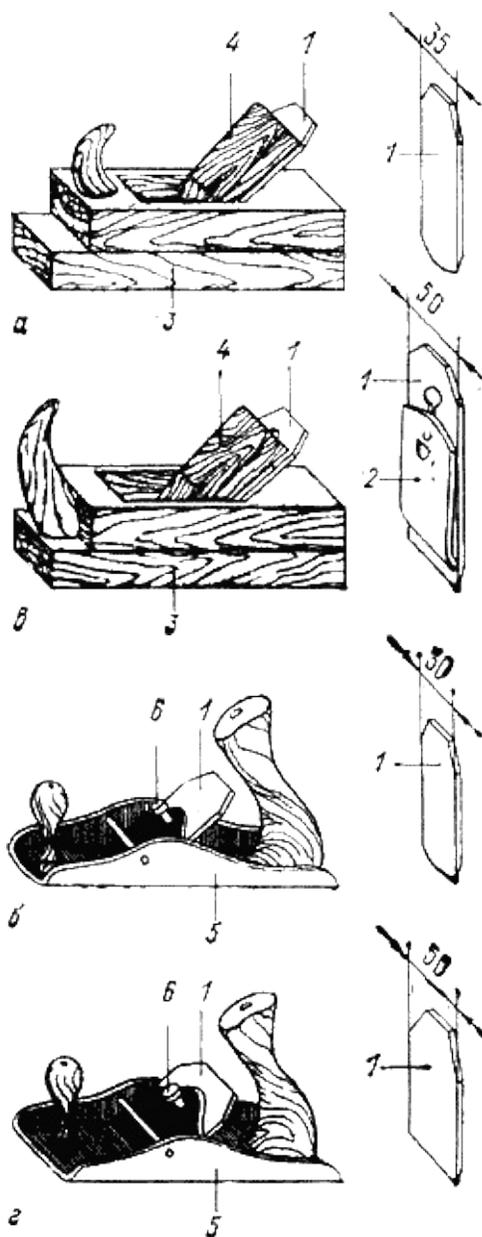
Инструменты для строгания: а — шерхебель деревянный; б — шерхебель металлический; в — рубанок деревянный; г — рубанок металлический; 1 — нож-резец; 2 — стружколоматель; 3 — колодка деревянная; 4 — клин; 5 — колодка металлическая; 6 — винт
